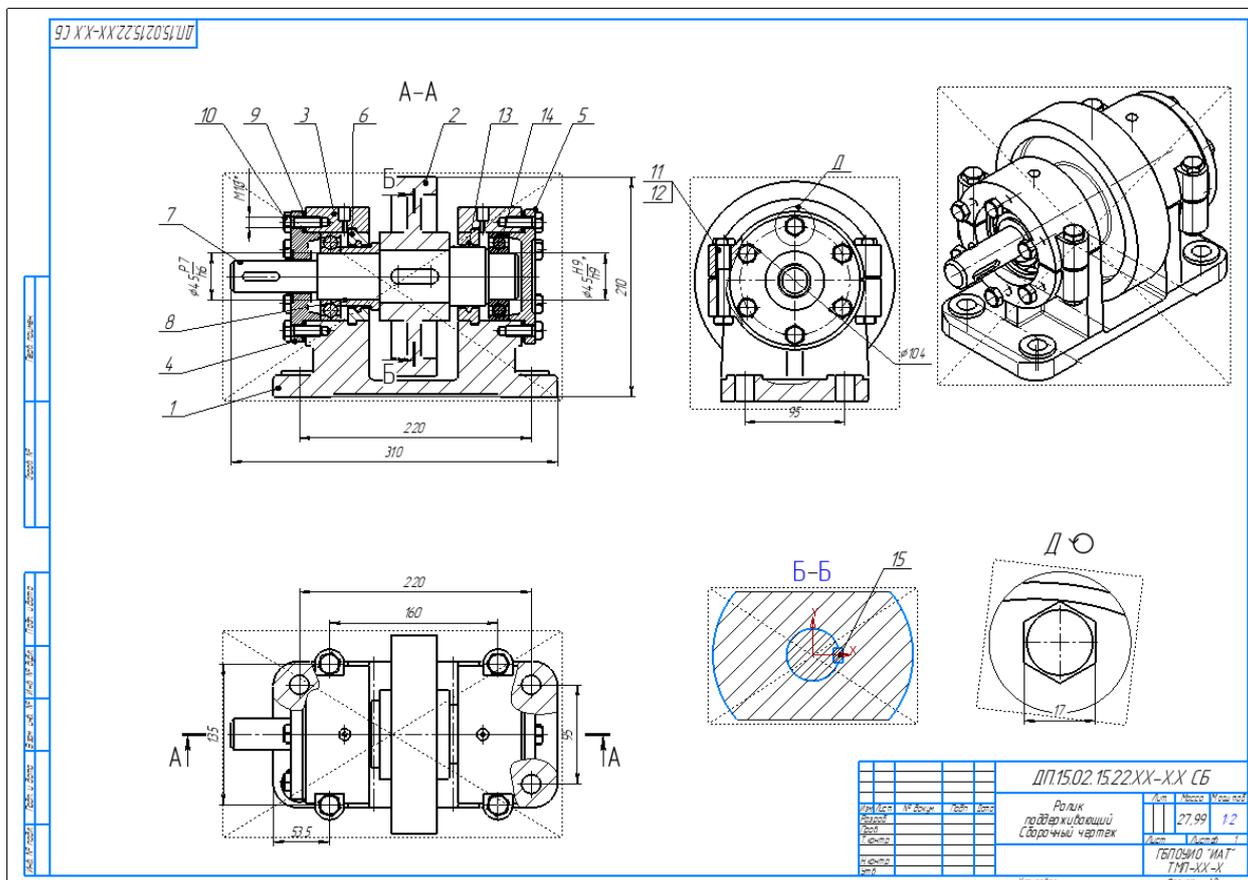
Пример оформления сборочного чертежа. Разработка спецификации
